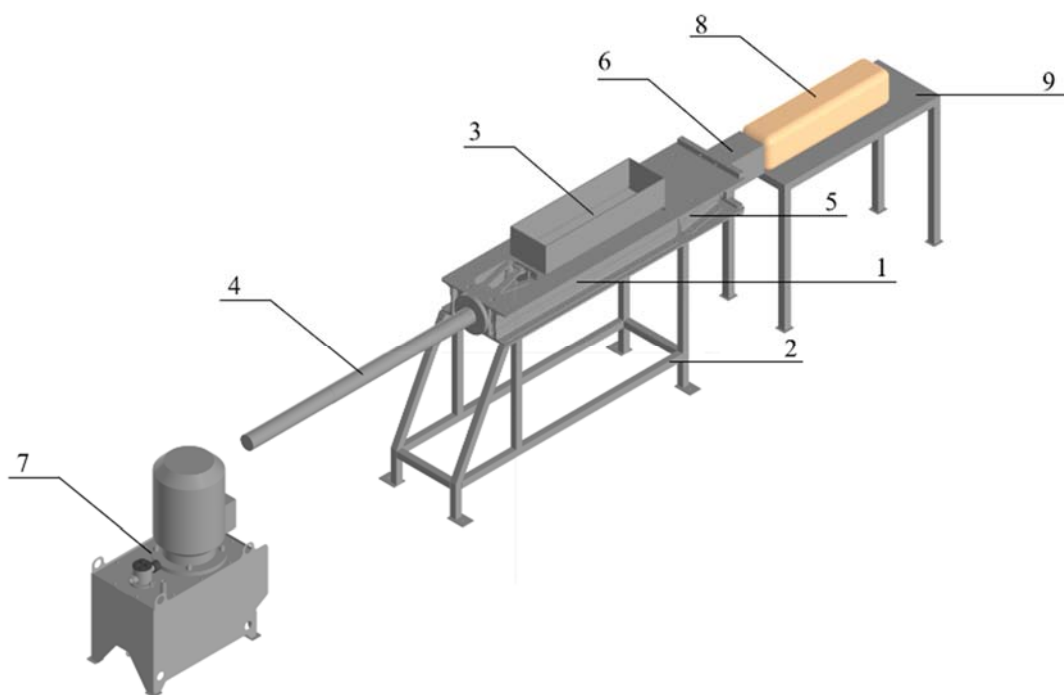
Общий вид устройства для наполнения пакетов грибным субстратом
